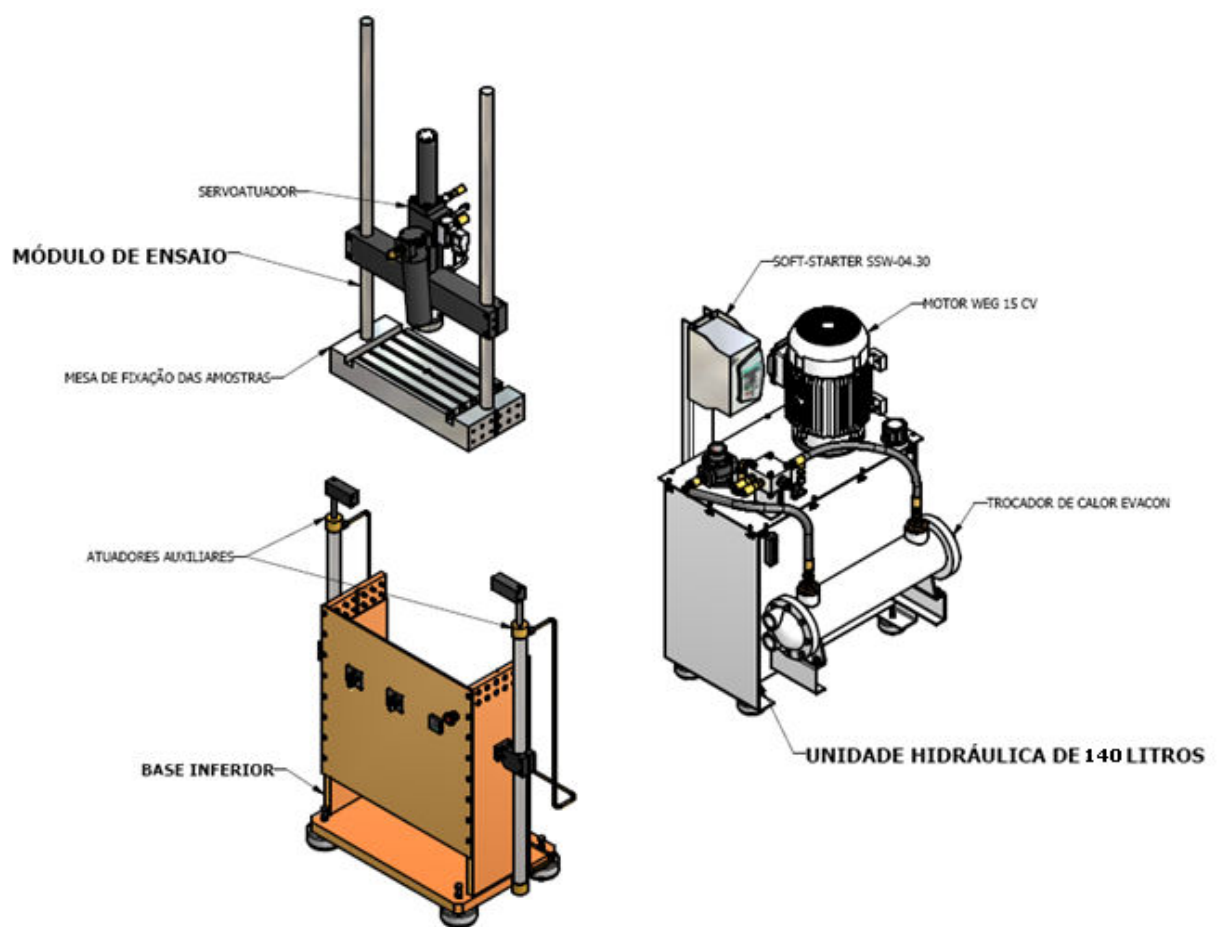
Vista em explosão da montagem da máquina de ensaios
